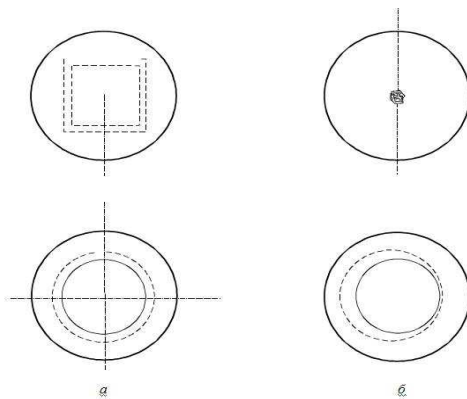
Схема поперечного расположения неметаллических включений после прошивания трубной заготовки полученной на установке непрерывного литья: а – равномерное расположение; б – смещение включений
